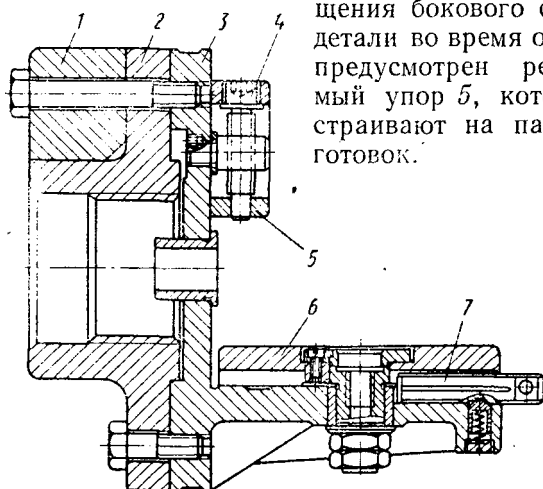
Универсально-наладочный угольник с поворотной планшайбой к токарным станкам
